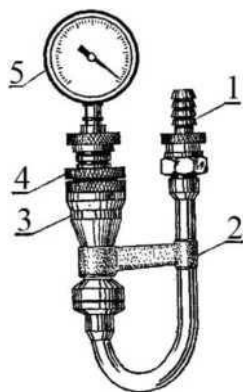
Індикатор КИ-4840: 1 - штуцер; 2 - ручка; 3 - корпус; 4 - регулювальна гайка; 5 - вакуумметр
